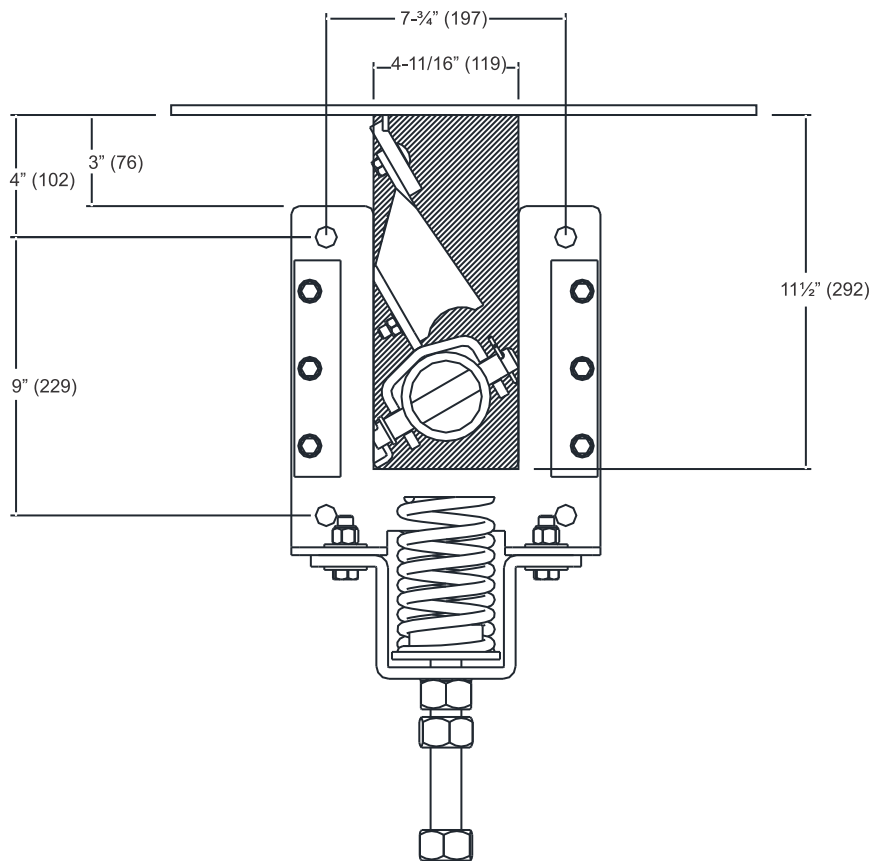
Dimensiones Agujeros de Soporte de Montaje
